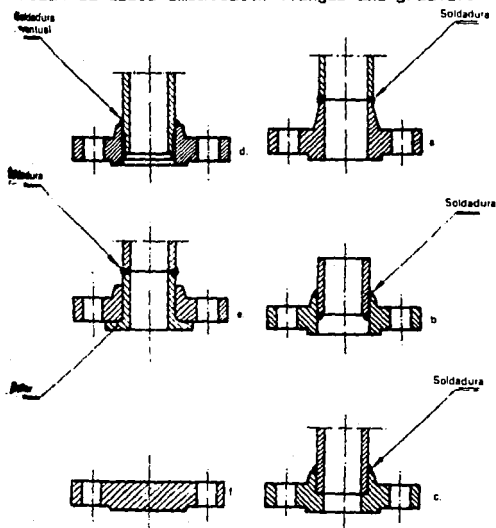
Tipos de bridas. a) Brida para soldar a tope (welding neck flange). b) Brida para soldar sobrepuesta (slip-on-flange). c) Brida para soldar a enchufe (socket welding flange). d) Brida roscada (threaded flange). e) Brida libre o loca (lap joint flange). f) Brida ciega (blind flange)
